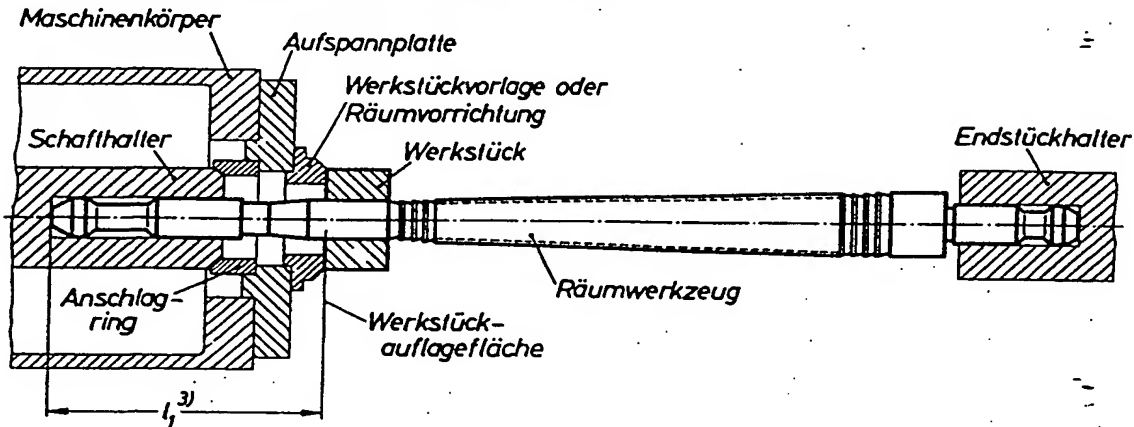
Räumwerkzeug mit Schafthalter und Endstückhalter
